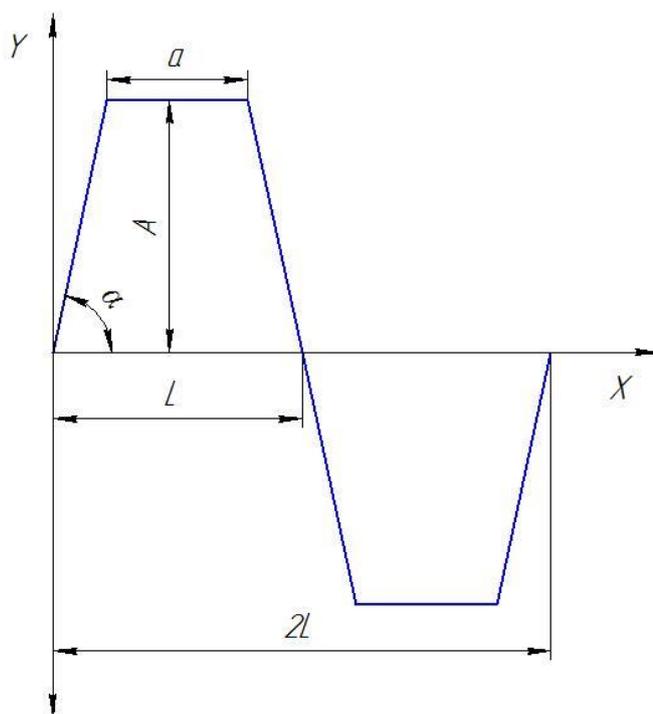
Схема колебаний сварочной проволоки
